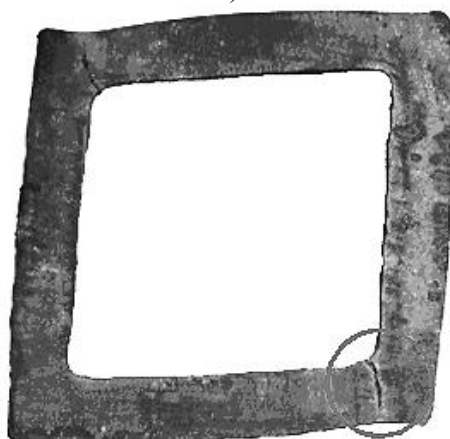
Пример прорыва корочки заготовки под кристаллизатором
